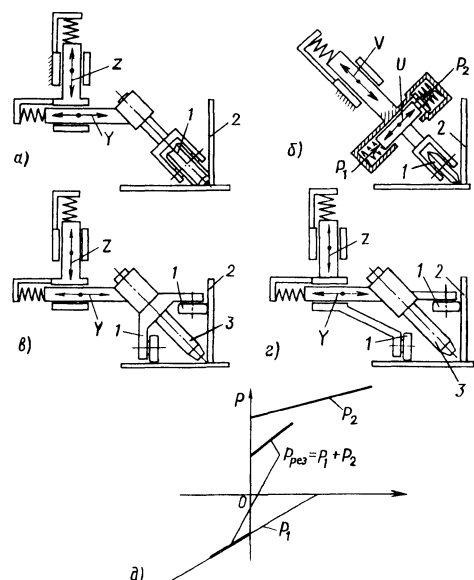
Схемы двухкоординатных устройств прямого копирования для сварки "в угол":
